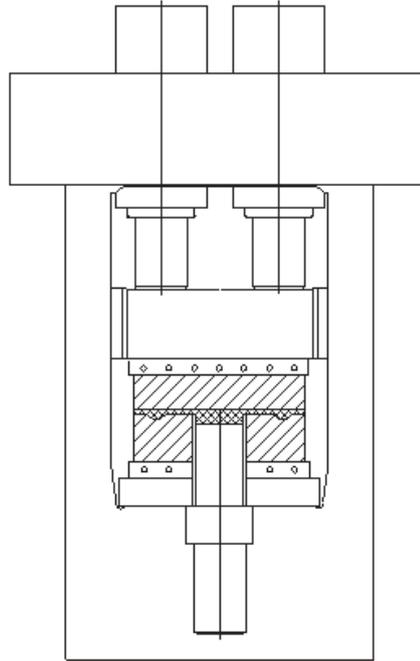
Presse zum Spritzpressen mit separatem Zylinder und mit Formmasse im formgebenden Hohlraum
